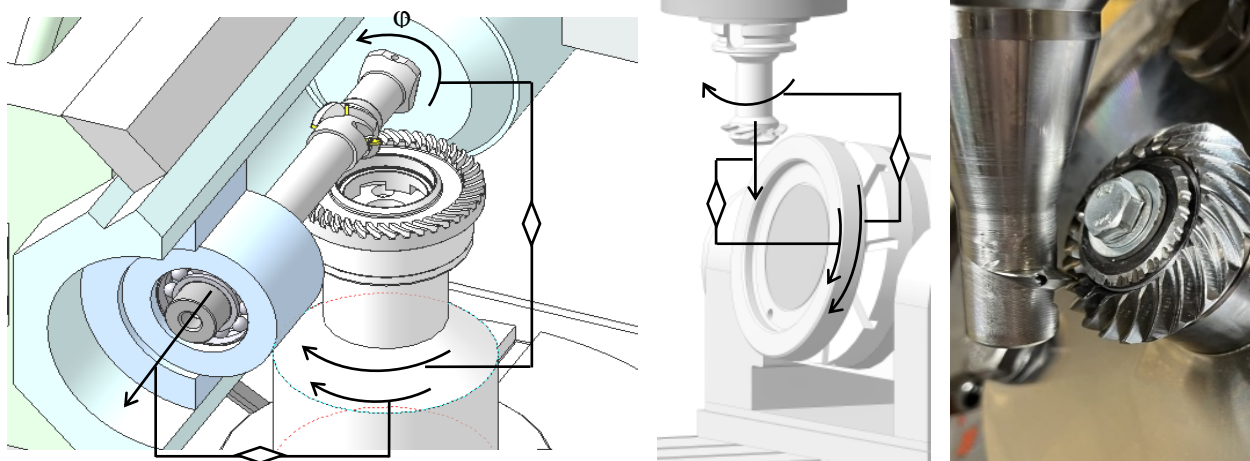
Нарезание спиральных зубьев обкаточной резцовой головкой на зубофрезерном станке (слева) и вертикальном обрабатывающем центре (справа)
